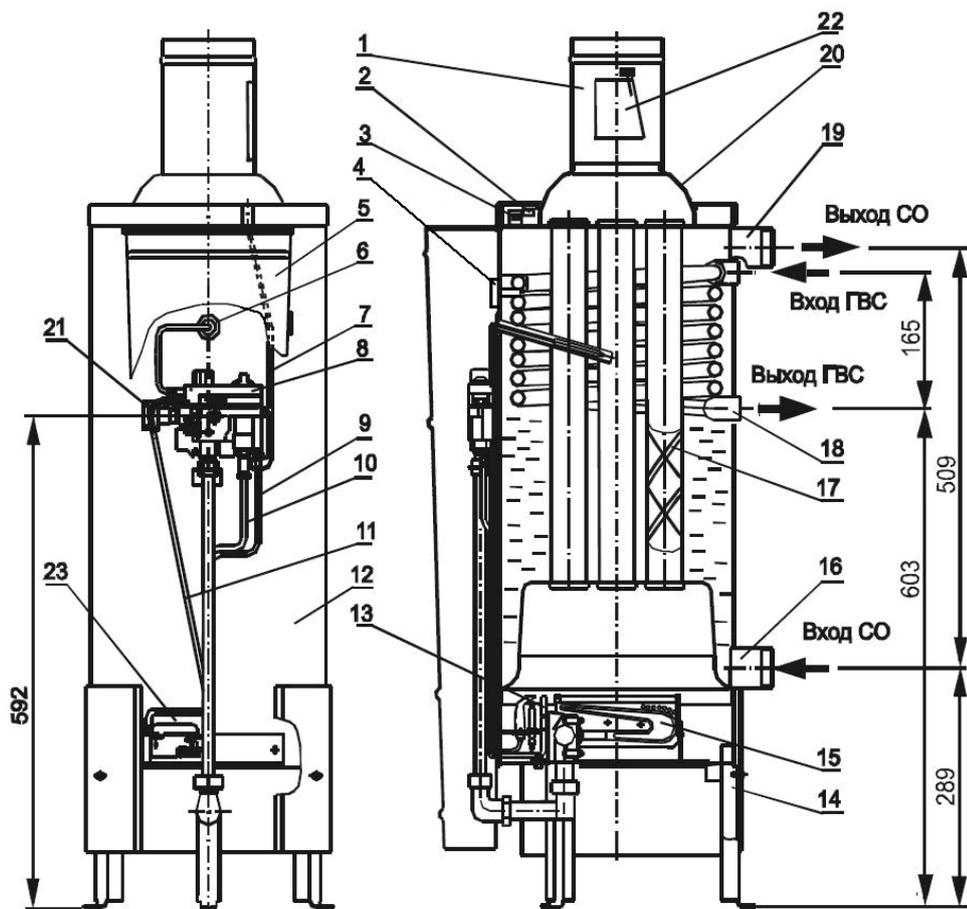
а. Котел отопительный газовый бытовой напольный комбинированный КОГВК-11,6 Honeywell
